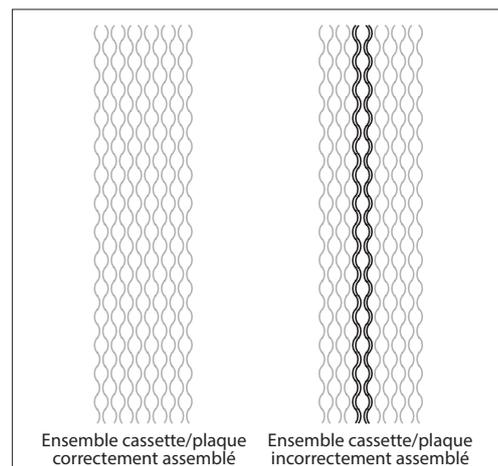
Ensemble de plaques correctement/incorrectement assemblé
